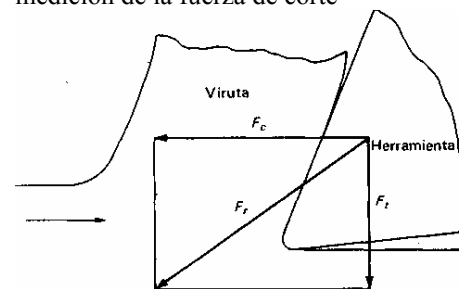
Componentes de la fuerza resultante (F_r) sobre la herramienta de corte.
